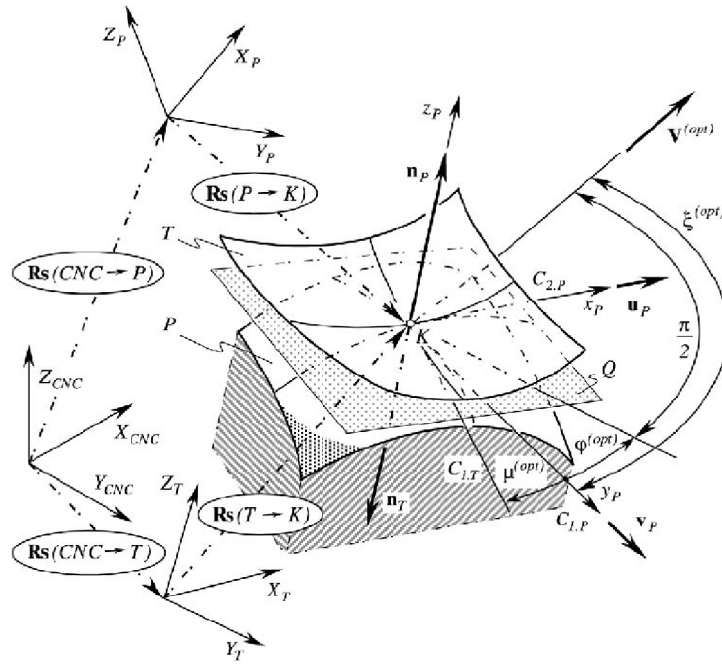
Positionnement relatif de deux surfaces [RADZEVICH 06]
